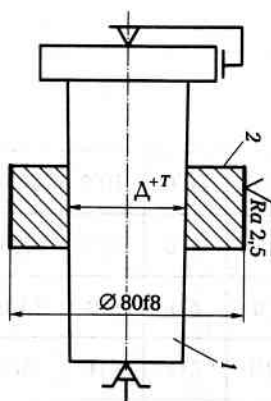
Схема установки заготовки на конусную оправку при шлифовании наружной цилиндрической поверхности
